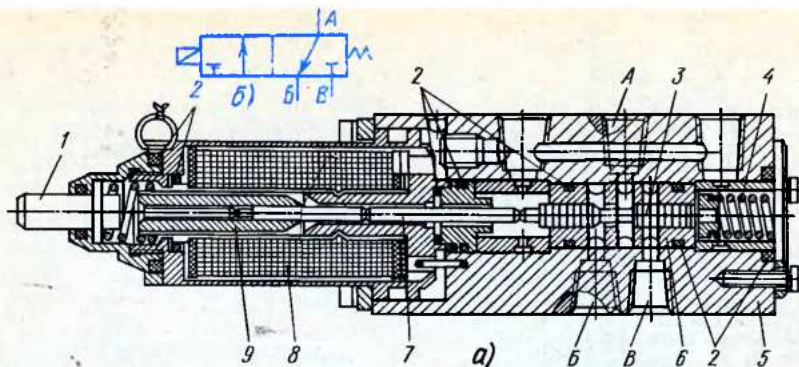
Двухпозиционный реверсивный гидрораспределитель автоматического управления гидроразмыкателем тормозов крана КС-3562Б (а) и его обозначение на схемах (б):
